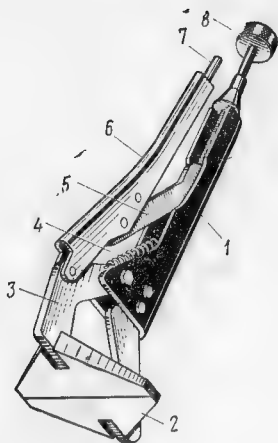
1 — корпус; 2 — губка; 3 — рычаг верхний; 4 — пружина растяжения; 5 — упор; 6 — кожух; 7 — ручка; 8 — винт регулировочный
